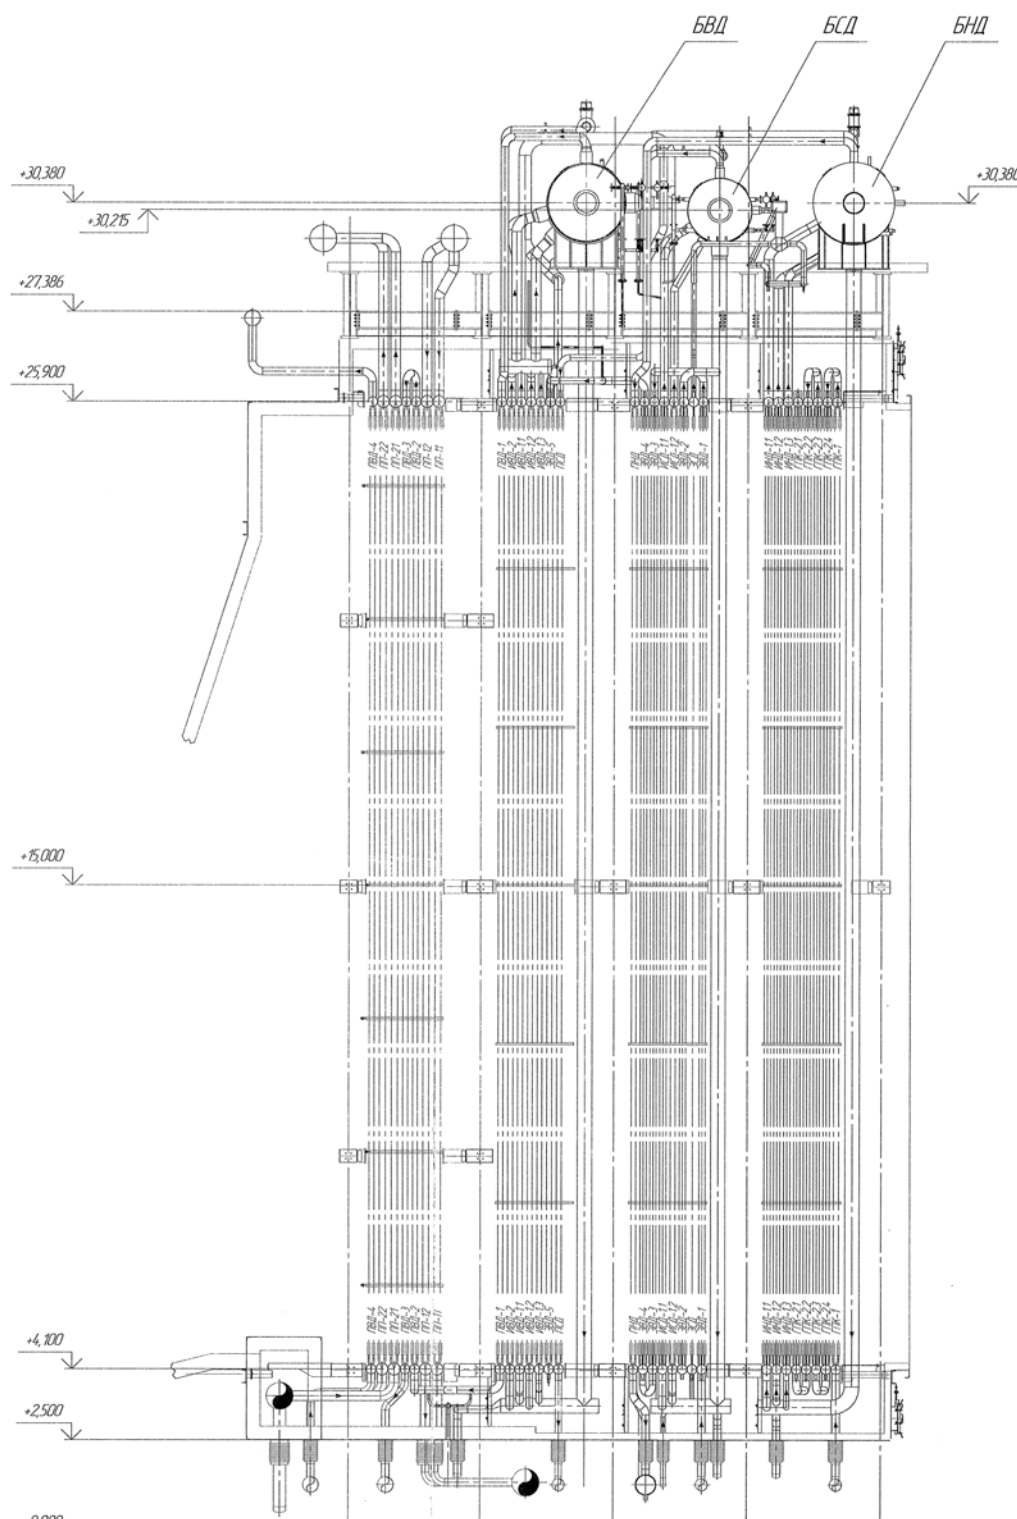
Компоновка поверхностей нагрева котла-утилизатора П-143
